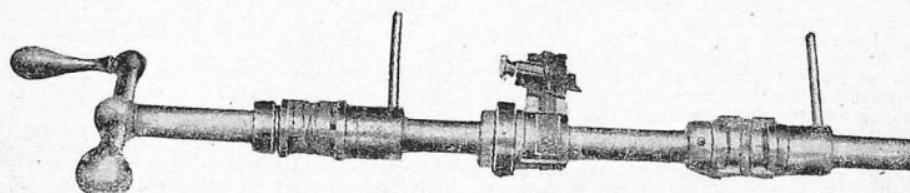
Инструмент с резцами для обточки поверхности подшипников
